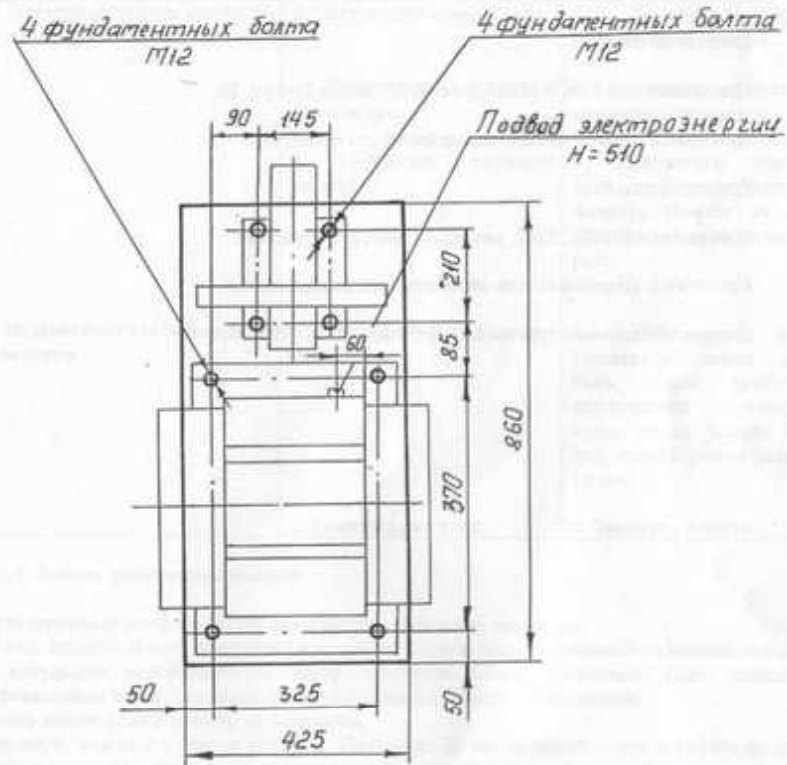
Схема установки станка мод.ВЗ-879-01
